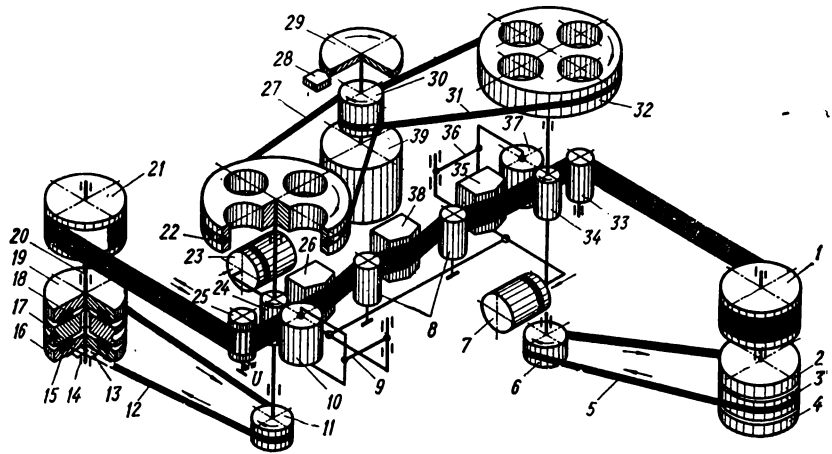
Кинематическая схема одномоторного бортового рулонного МТЛ с реверсивным движением магнитной ленты.
